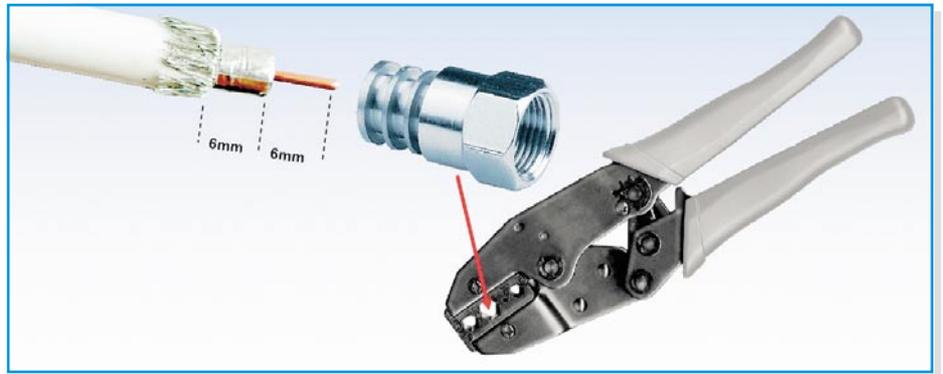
Drei Schritte zur Crimpverbindung: Absetzen des Kabels – Aufschieben des Crimpsteckers – Aufquetschen des Crimpsteckers mit der Crimpzange
